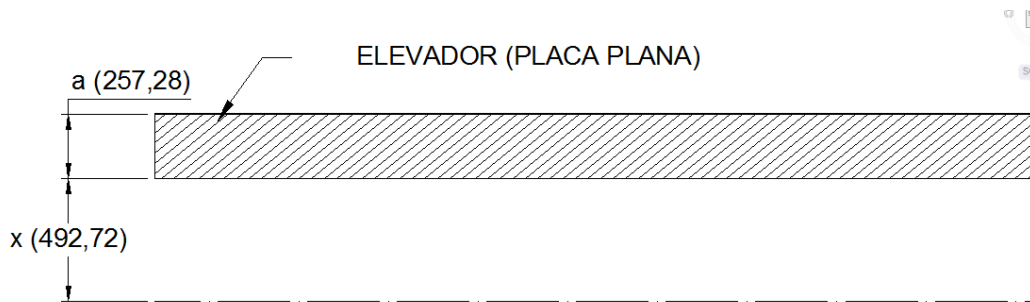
Inercia de placa plana aplicando teorema de Steiner (elevador)
